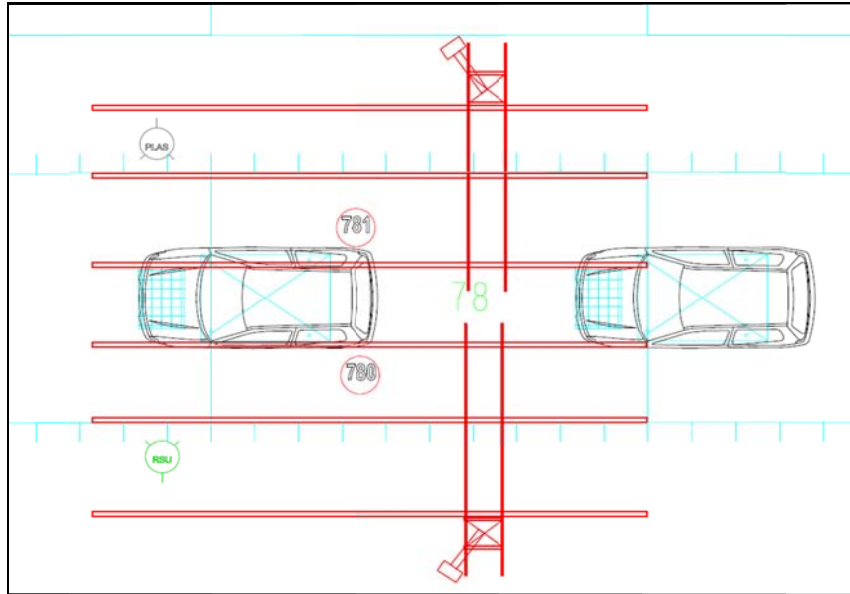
Layout manipuladores montaje butacas (opción 1)
